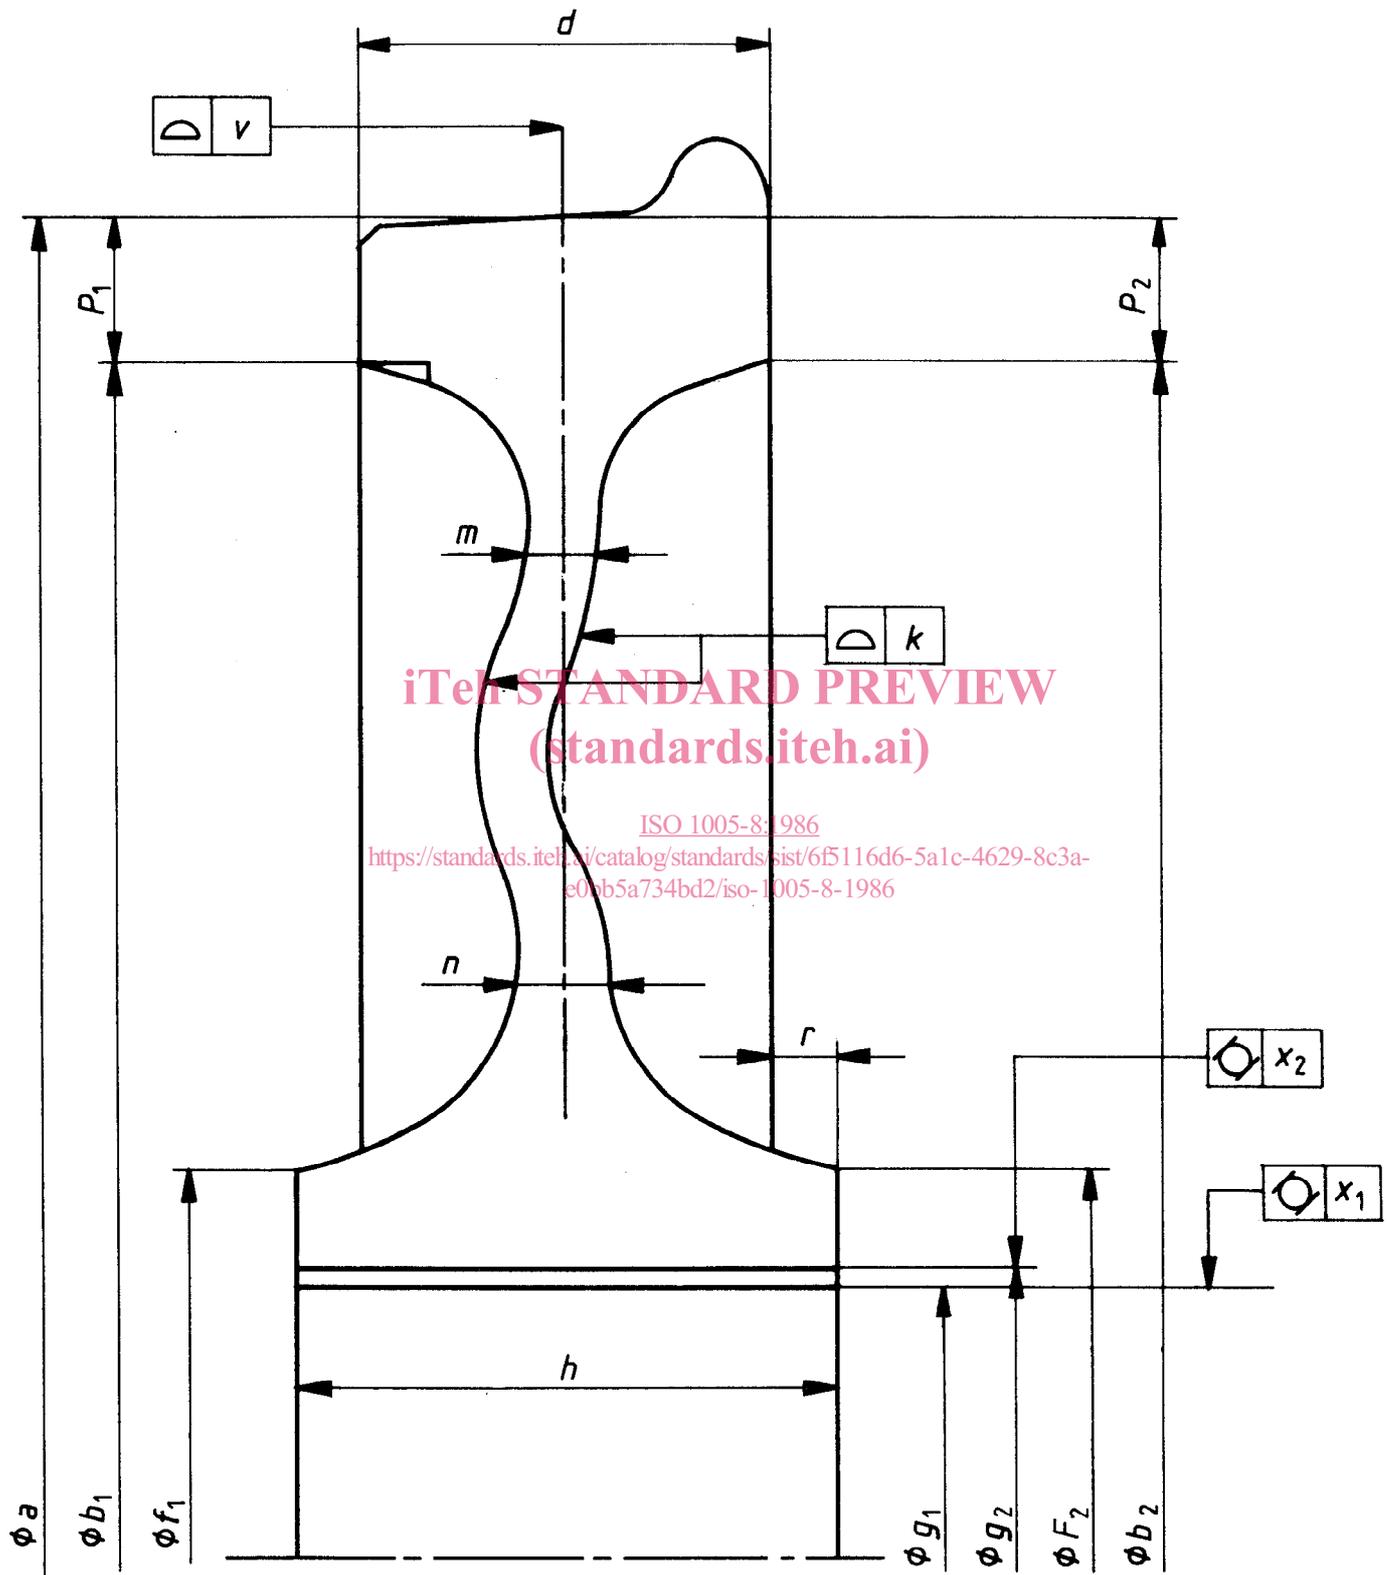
Symboles des caractéristiques dimensionnelles prescrites au tableau 4 pour les parties «finies» et à l'état «prêt à assemblage» des roues monoblocs forgées, laminées ou moulées
